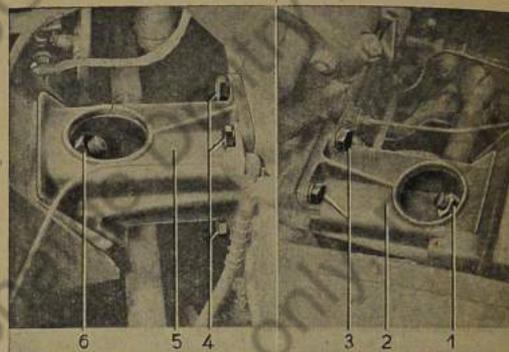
Rechten und linken Bock für Getriebeaufhängung abschrauben
